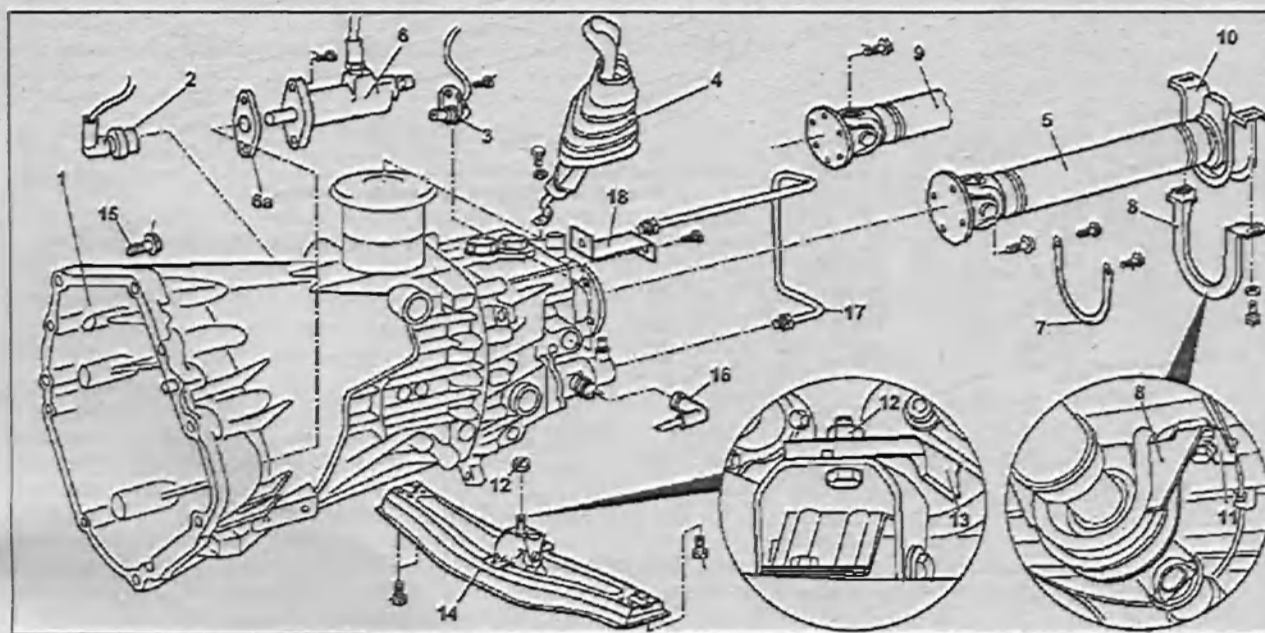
Снятие и установка механической коробки передач 711.603/612/613:
